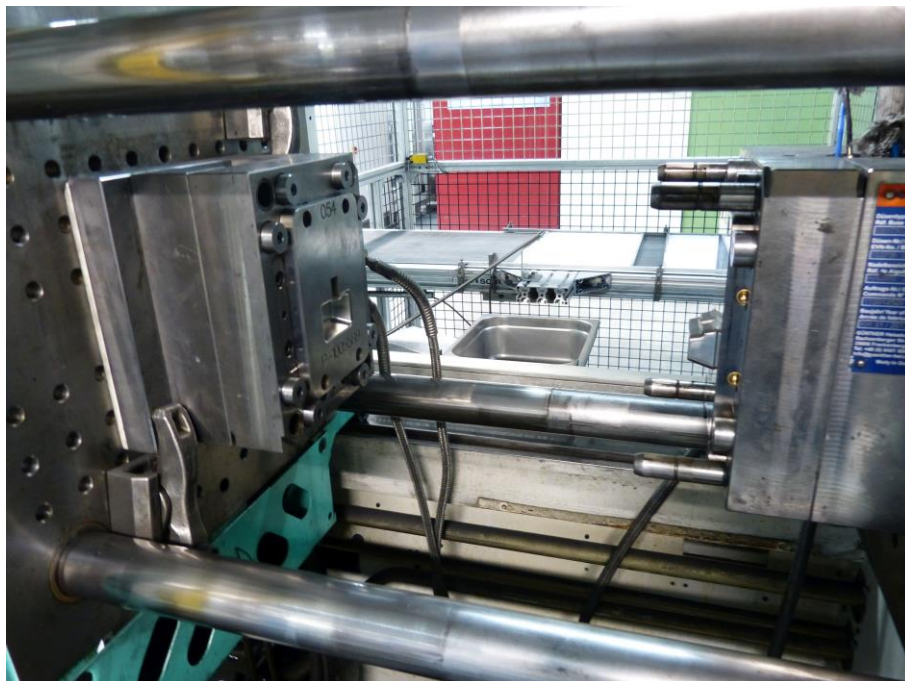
zweites Spritzgusswerkzeug, offen, eingebaut in Spritzgussmaschine
